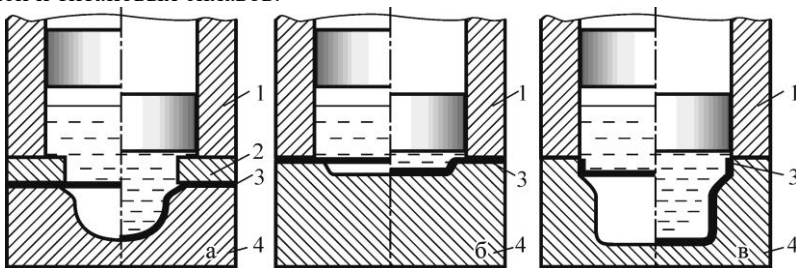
Основные технологические схемы пневмоударной штамповки жидкостью: а и в – вытяжка из плоской и пространственной заготовок; б – формовка: 1 – рабочая камера; 2 – прижим; 3 – заготовка; 4 – матрица
